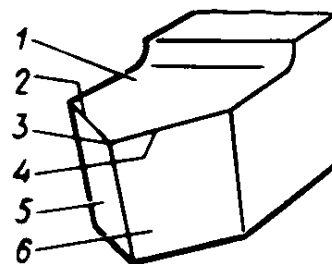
Элементы режущей части токарного резца: 1 – передняя поверхность, 2 – вспомогательная режущая кромка, 3 – вершина режущей части, 4 – главная режущая кромка, 5 – вспомогательная задняя поверхность, 6 – главная задняя поверхность
